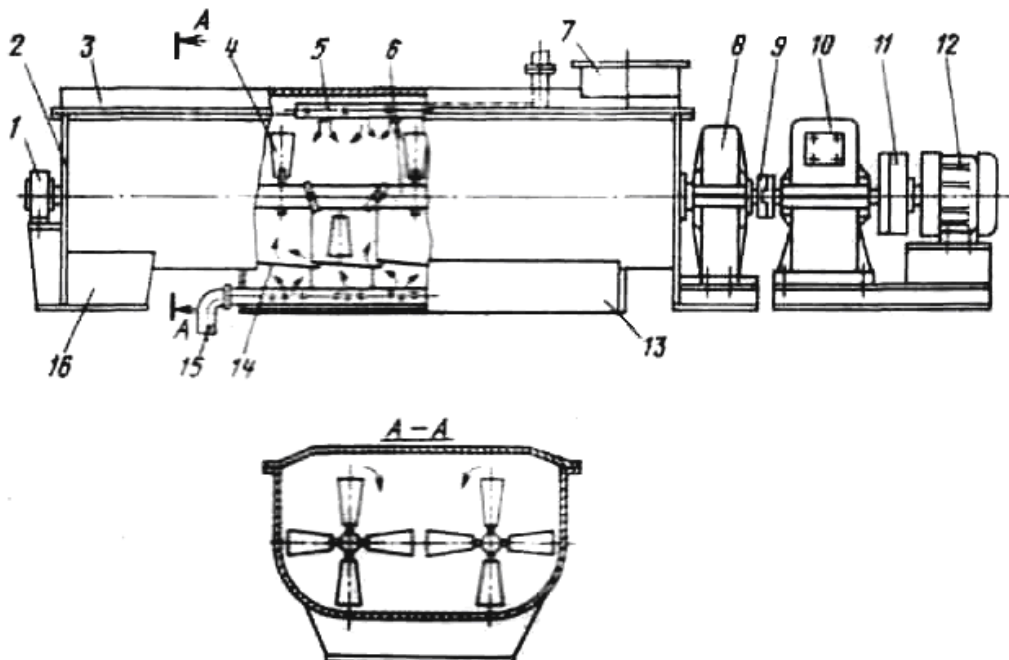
Двухвальный смеситель непрерывного действия
